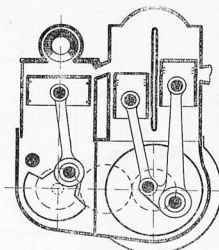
Схема двигателя ДКВ (250 куб. см)
